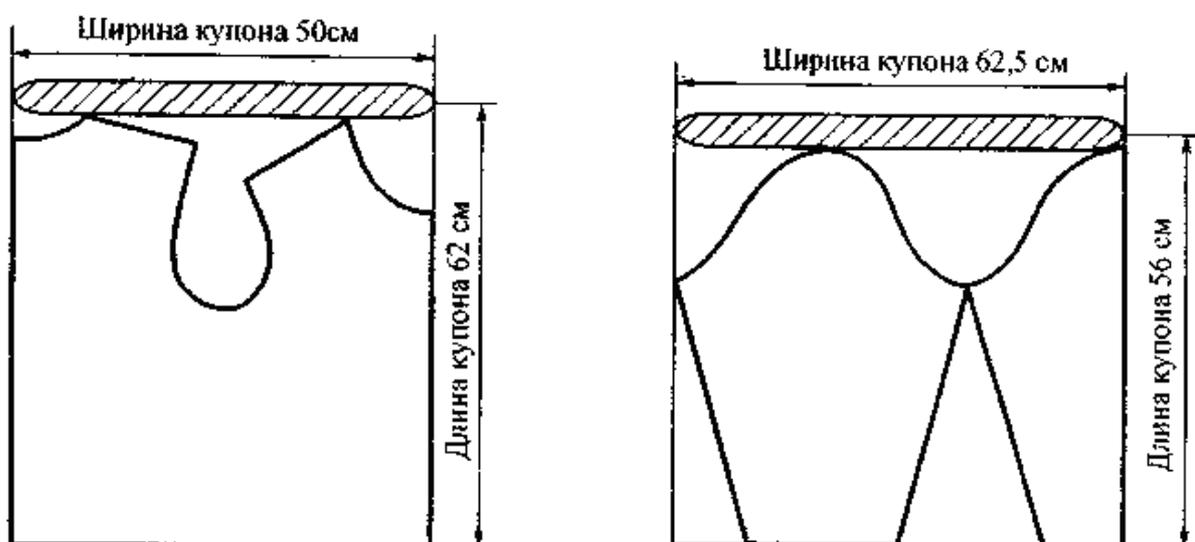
Форма купонов детали для изготовления трикотажных изделий полурегулярным способом
